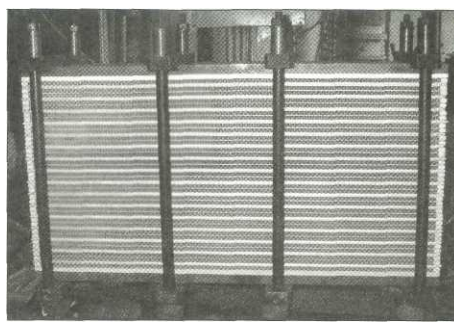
Пакет деталей ПРЕ, зібраний для паяння
